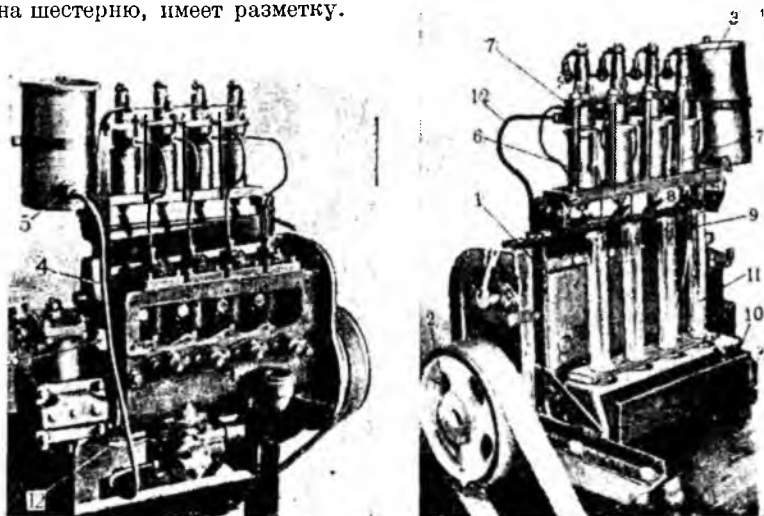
Настольный стенд для регулировки насосов ЧТЗ:
